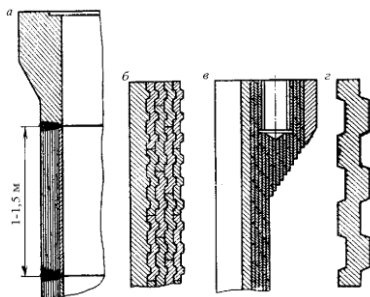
Узлы многослойного (а), витого (б, в) корпусов и профиль ленты (г) для навивки
